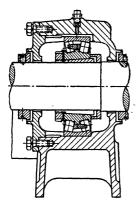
Установка радиального двухрядного сферического роликоподшипника в отдельном корпусе
